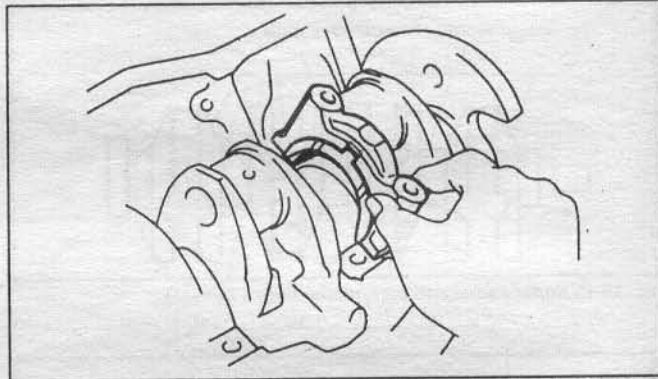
б Осевой подшипник в крышке средней шейки. Масляные канавки устанавливать наружу.
